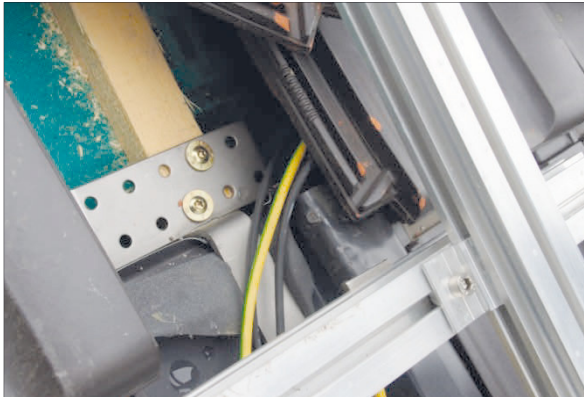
Brandschaden aufgrund nicht fachgerechter Kabelverlegung
